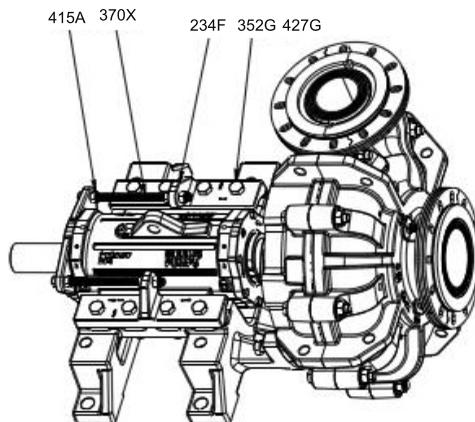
Sécuriser la plaque d'ajustement du cadre de roulement
